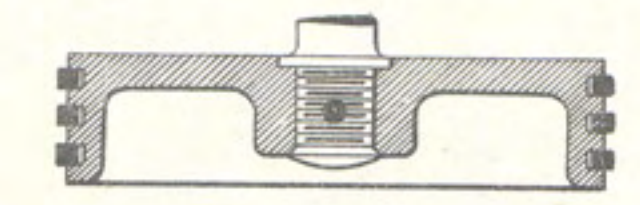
Piston suédois assemblé à sa tige par rivures.
